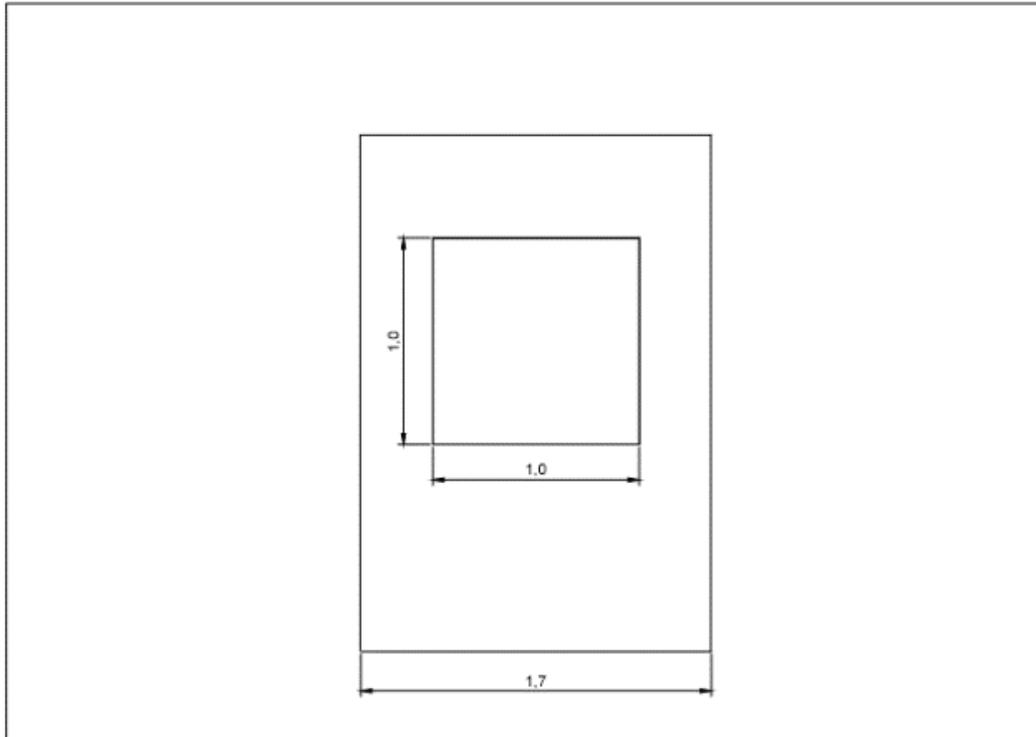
Dimensiones de la cara lateral de la cabina acústica para la planta Barro Morado II
